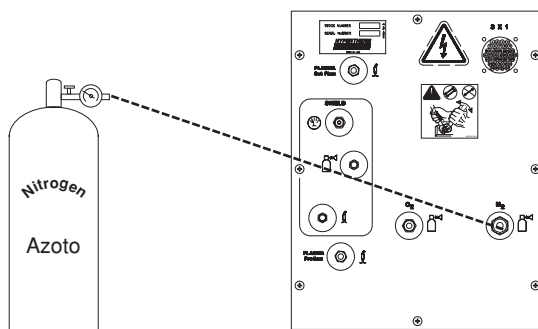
Alimentazione dell'azoto all'ingresso N₂ della consolle del gas
